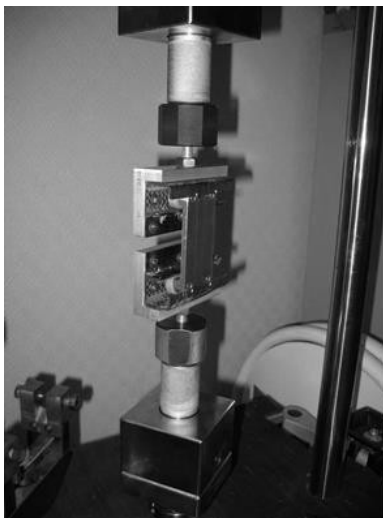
Общий вид захвата приспособления в испытательной машине
